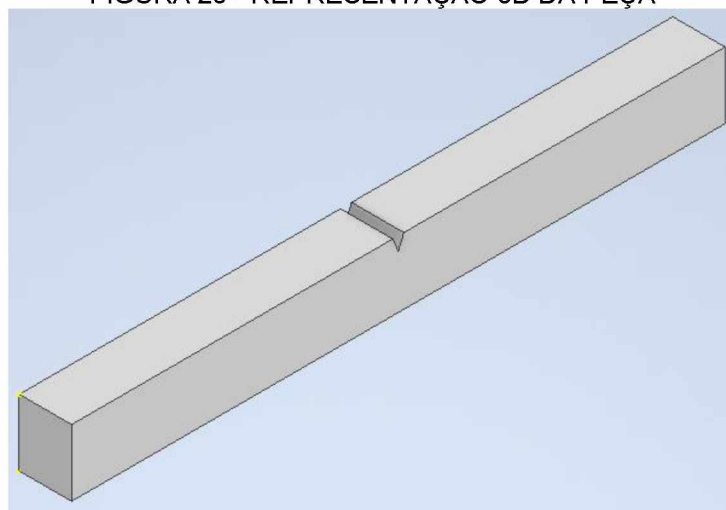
DESENHO TÉCNICO DA PEÇA
